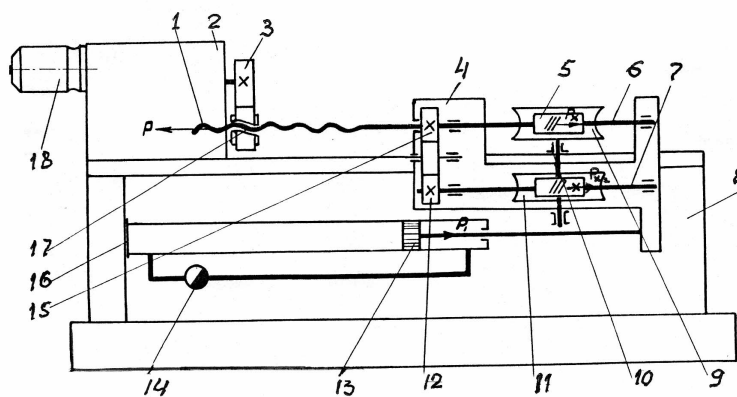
Схема механізму подачі зубофрезерного верстата
